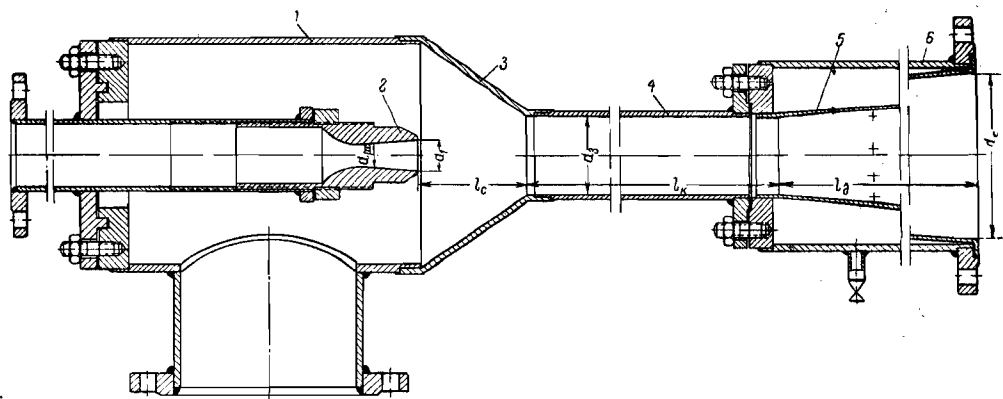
Пароструйный компрессор конструкции ВТИ.
